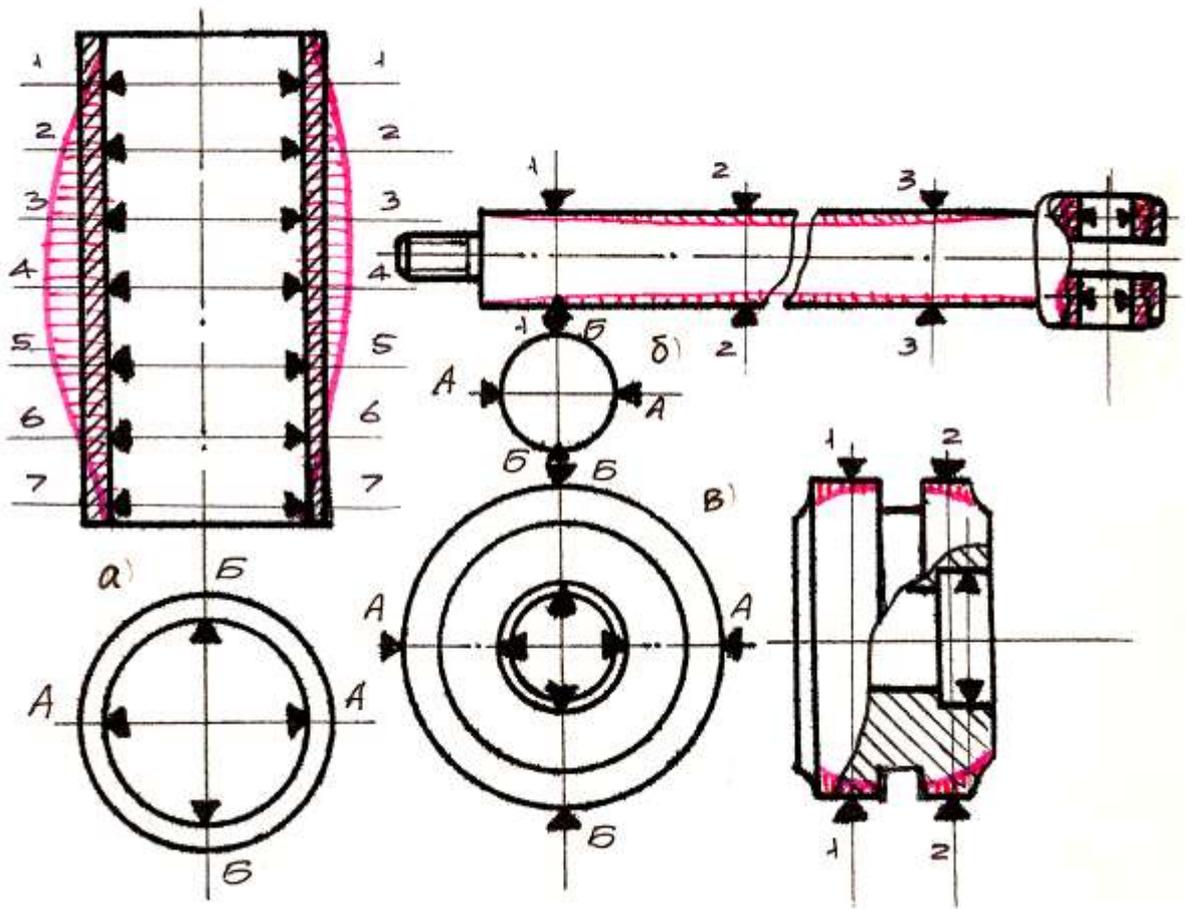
Схемы контроля размеров деталей гидроцилиндров:
